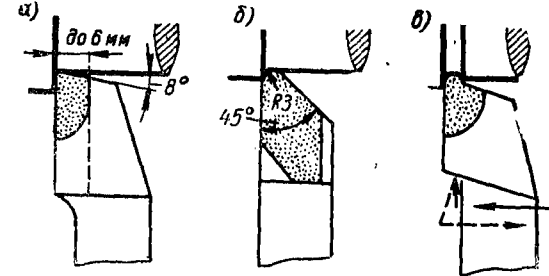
Комбинированные резцы для обработки ступенчатых поверхностей.
